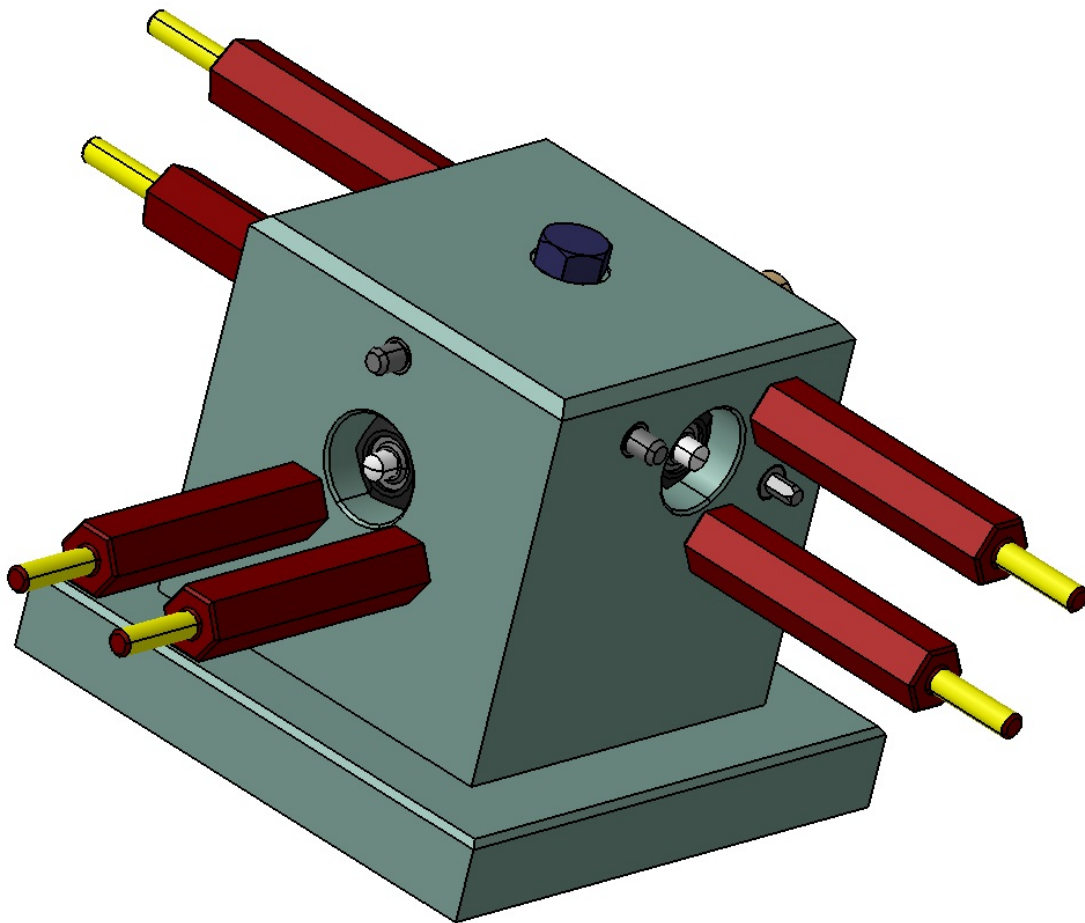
Detail a princip vysouvacího mechanismu obrobku z přípravku – směr pohledu z vnitřní strany (žlutou barvou jsou znázorněny závity)
